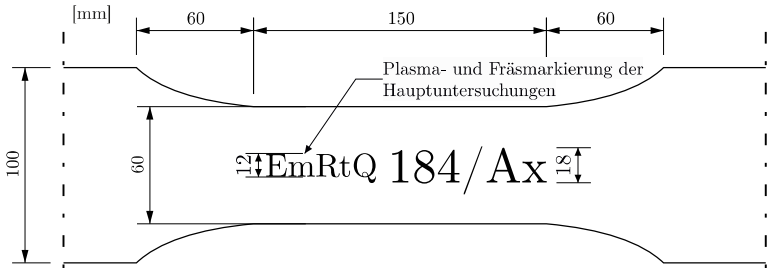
Gewählte Markiergeometrie für plasmamarkierte sowie gefräste Versuchskörper
